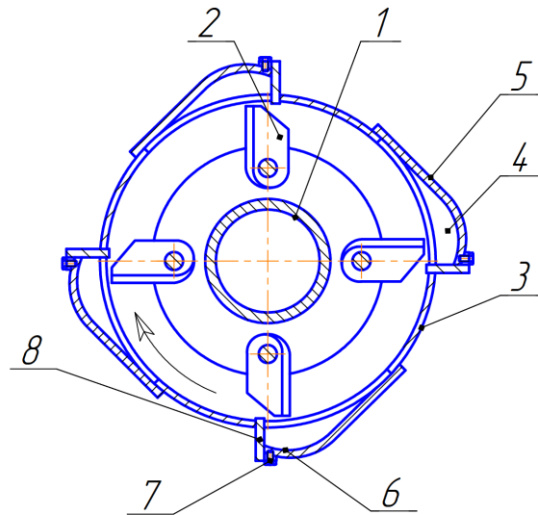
Дробарка: 1 – ротор; 2 – робочий орган; 3 – камера подрібнення; 4 - камера вихрова; 5 – стінка; 6 – кутова частина; 7 – гвинт; 8 – стінка.
